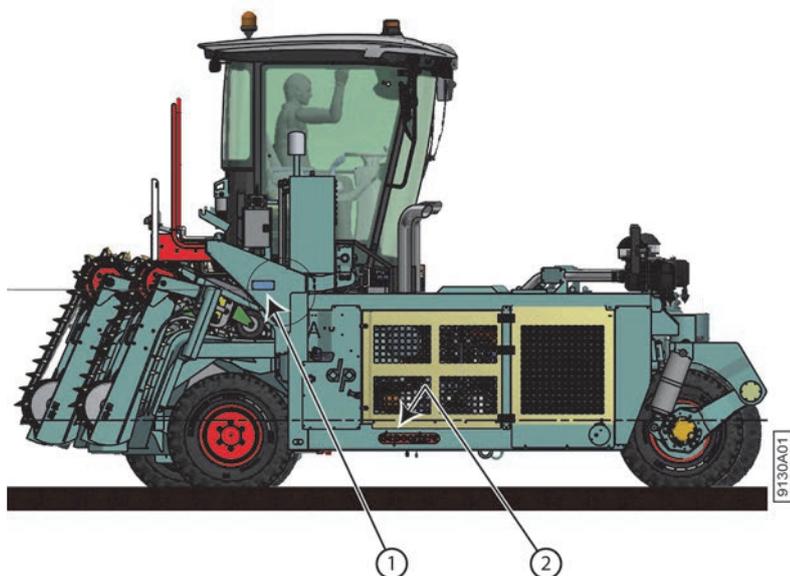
Emplacement de la plaque d'identification et du numéro de châssis sur la machine
